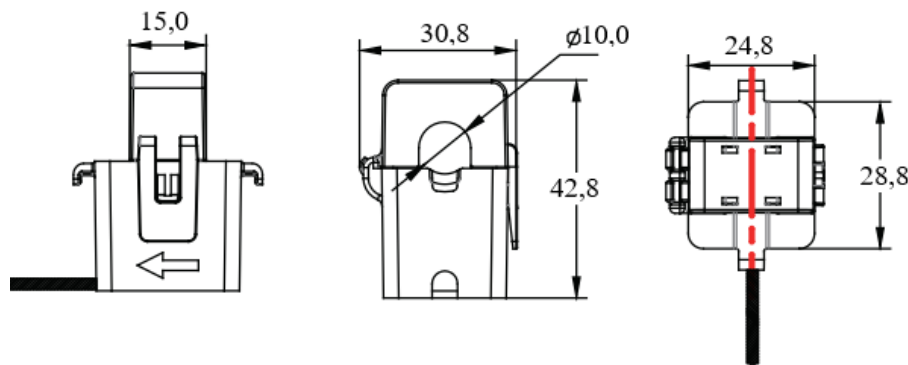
Внешний вид и габаритные размеры датчика SCT50
